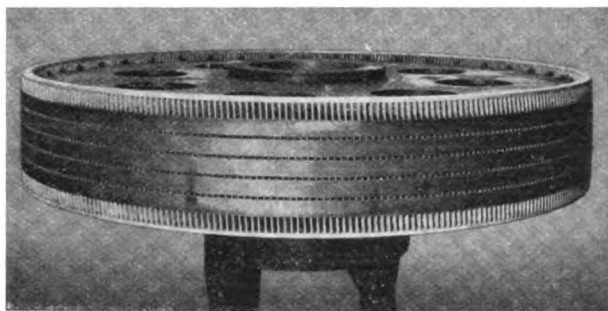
Kurzschlußläufer mit Aluminiumkäfig für Kolbenverdichterantrieb 500 kW, 5000 V, 122 U/min.
